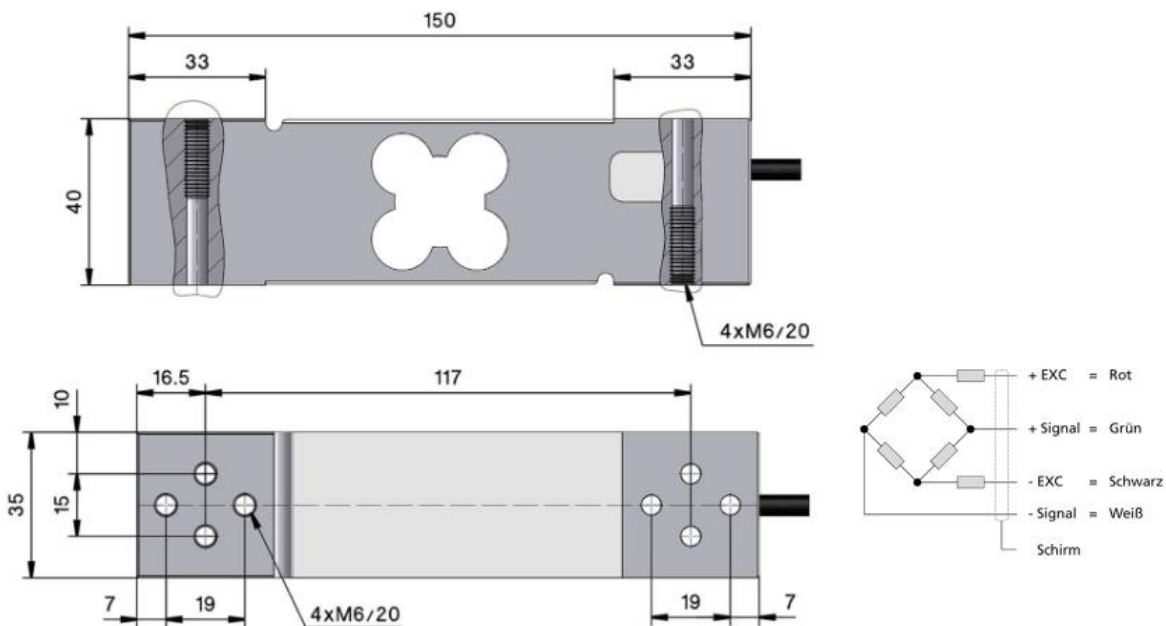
Zeichnung Bosche Wägezelle H30A
